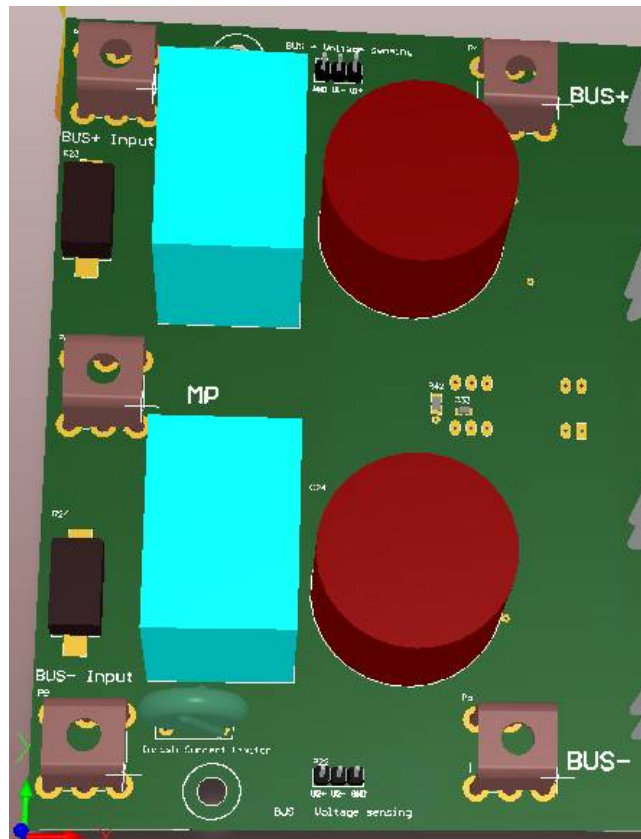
Edición de PCB: Vista 3D parte izquierda plano superior.
